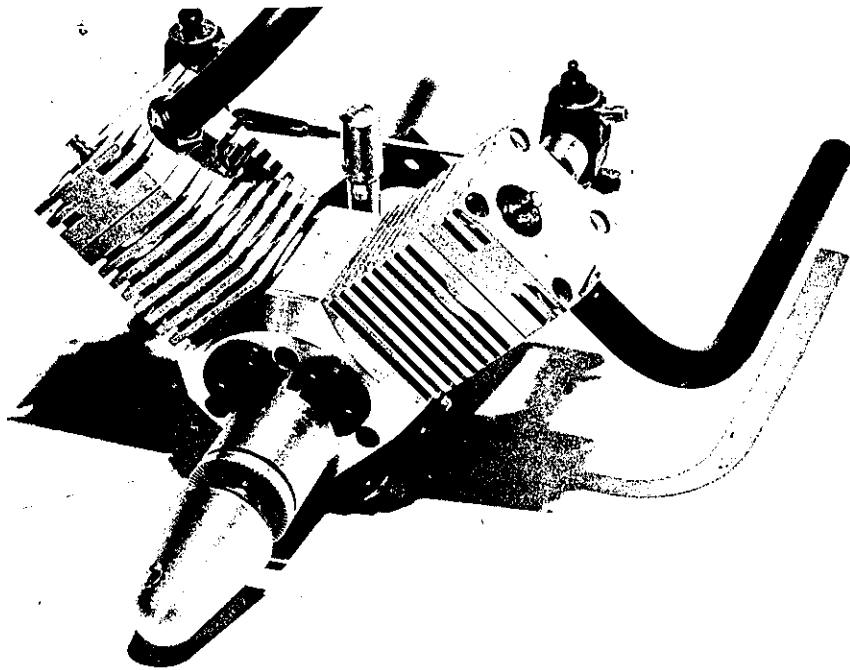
Ein V-Motor mit 90°-V-Winkel. Der Motor besteht aus zwei Schiebermotoren der Bauart Dylla mit rotierenden Zylindern und Flachdrehschiebern im Zylinderkopf. Der Motor hatte 11,5 ccm Hubraum und eine Leistung von 480 Watt bei 11 000 U/min. Baujahr 1977/78.
